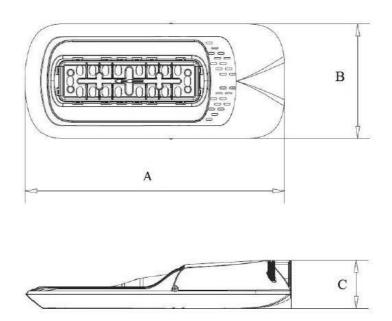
Вид светильника ДКУ61 (корпус Winner)
